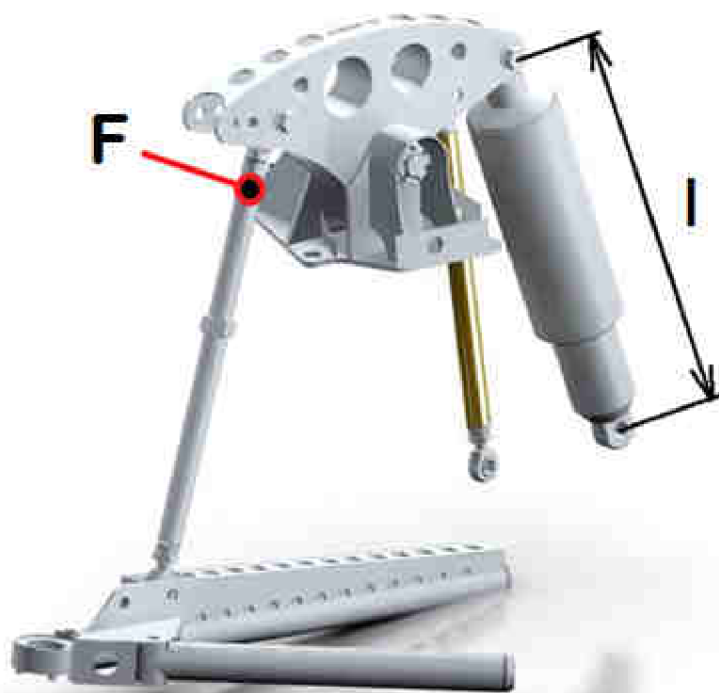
Uložení tlačné tyče a tlumiče/pružiny ve vahadle
